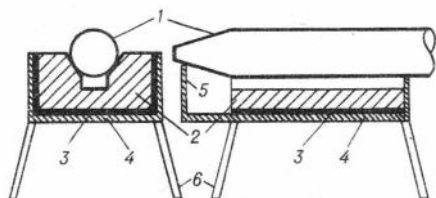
Контрольно-калибровочное устройство 1 - -глубинный прибор; 2 - -алюминий; 3 - свинец; 4 - -корпус; 5 - ограничитель, фиксирующий положение глубинного прибора; 6 - -ноги.
